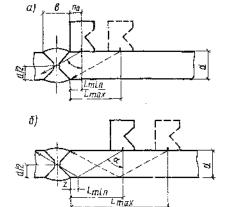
Схемы контроля стыковых сварных соедипений
